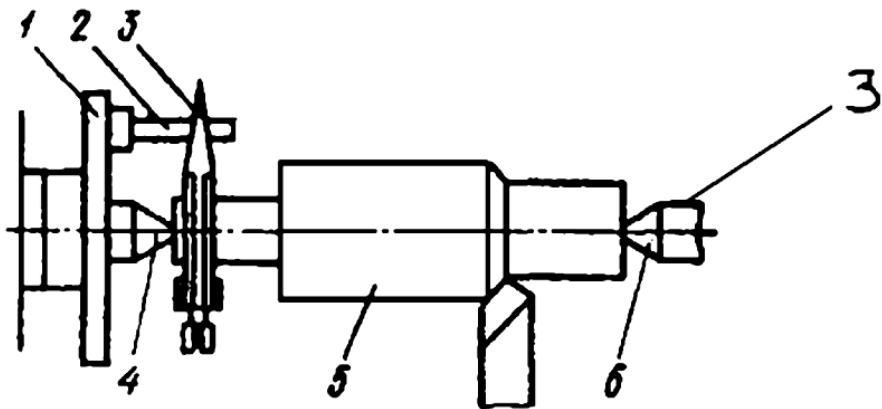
Обробка в центрах з приводом заготовки від повідкового патрона
